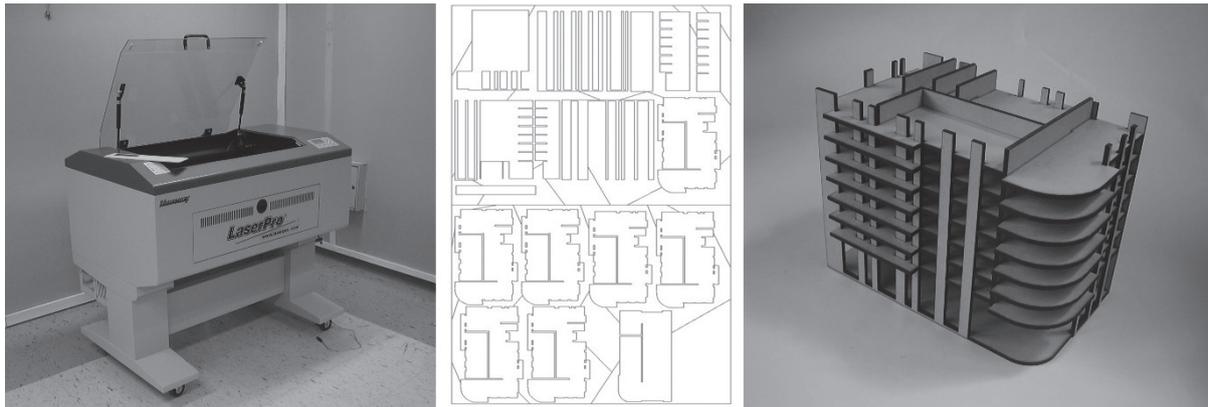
Cortadora laser, planos de corte y modelo constructivo de edificio
